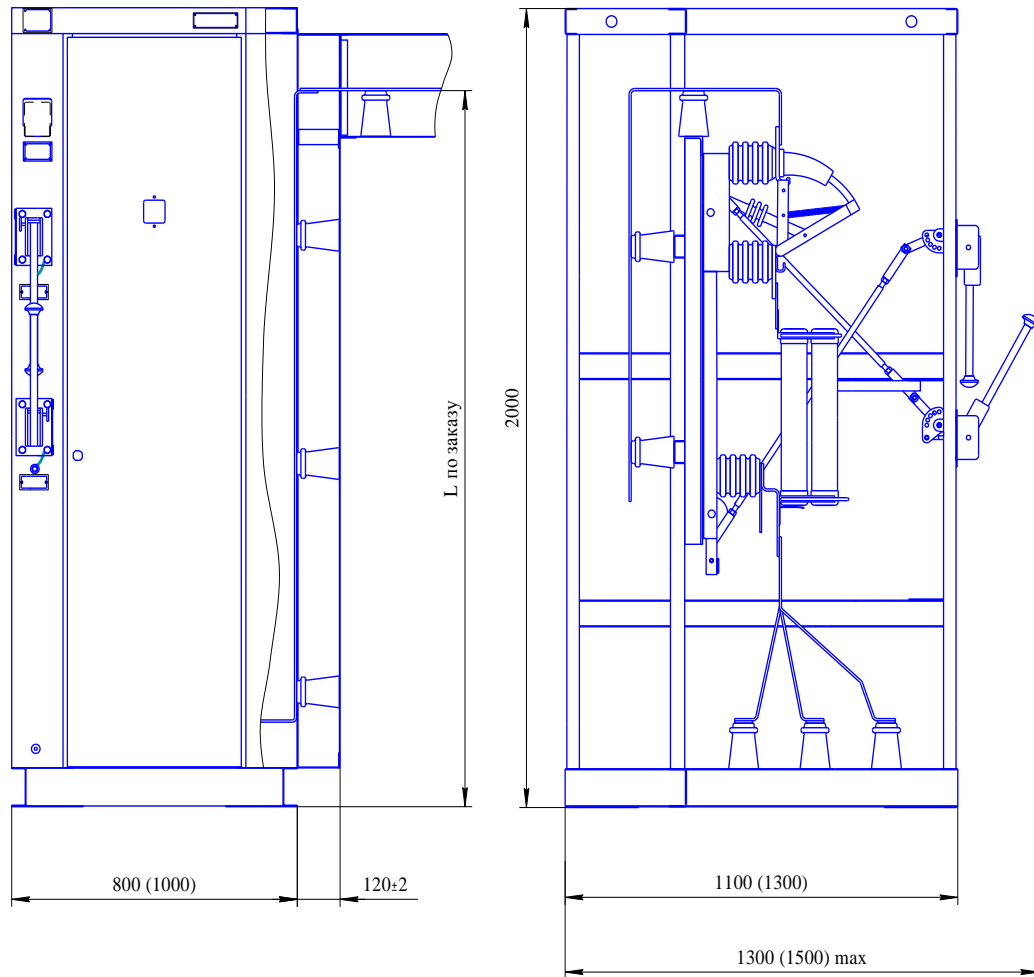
Габаритные размеры камеры КСО - 303 - 04
